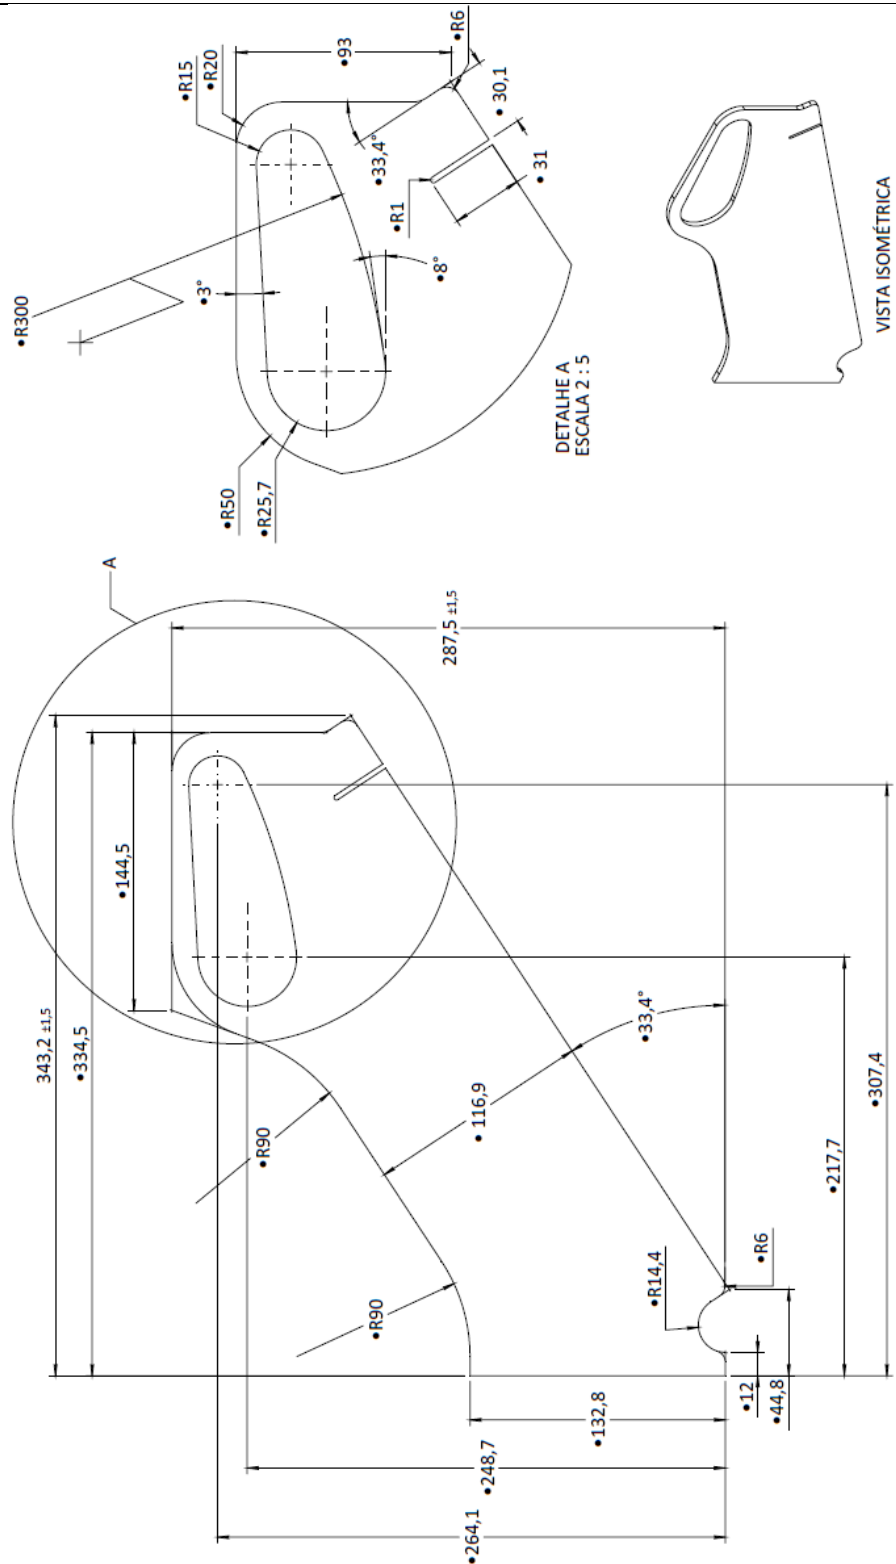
Detalhe dimensional do reforço de ligação da travessa e suporte fronta Air Super H210
